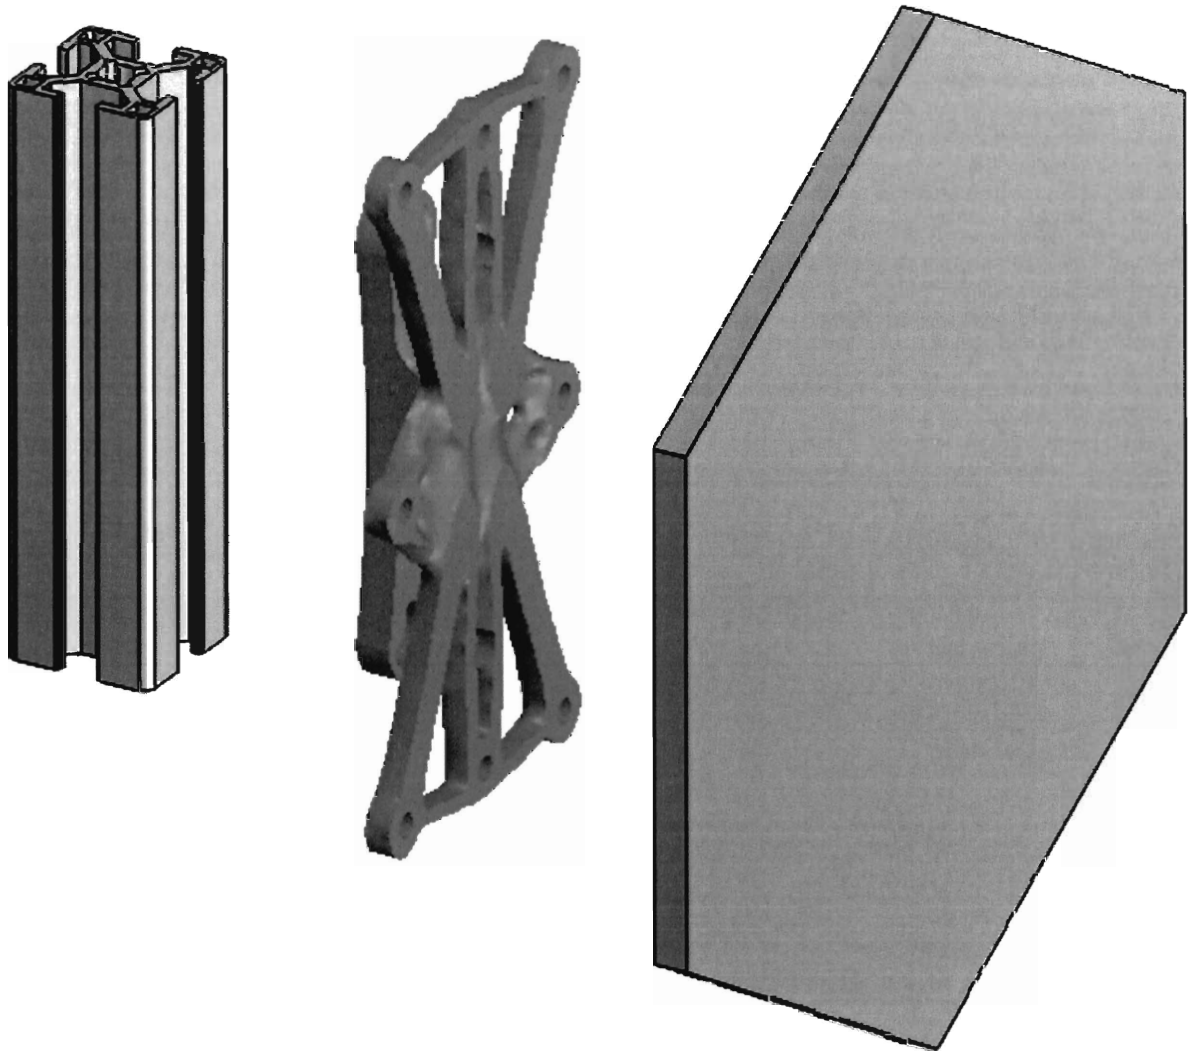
Vedere izometrică explodată ansamblu – TIP 1
